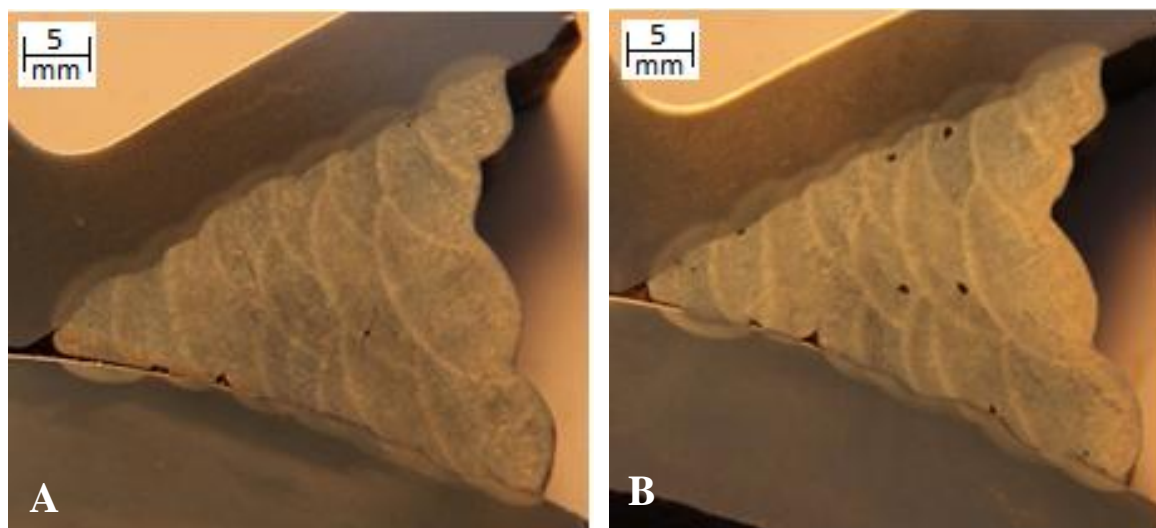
Macrografias do corpo de prova soldado com o processo RMD na posição horizontal
